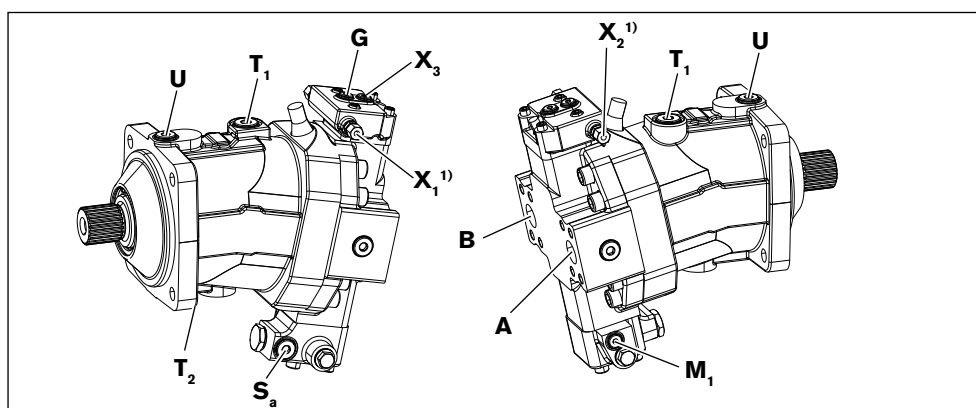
Vue d'ensemble des raccords A6VM avec réglage DA et valve de rinçage, raccords de service à l'arrière
